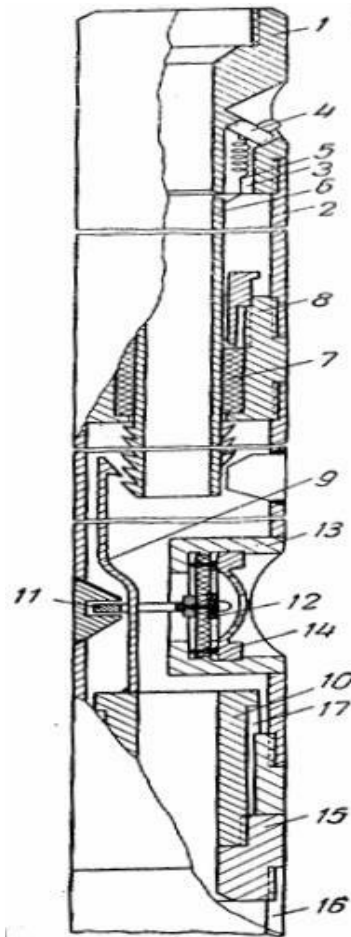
Забойный гидравлический дробопитатель:
